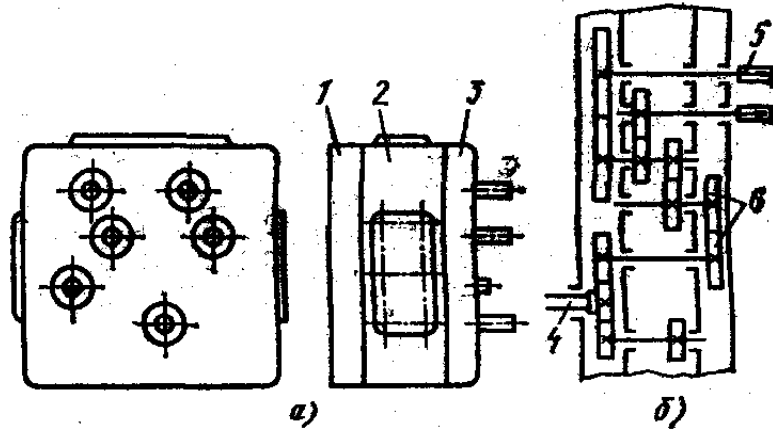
Шпиндельні коробки: а – загальний вид; б - розгортка по вісям
